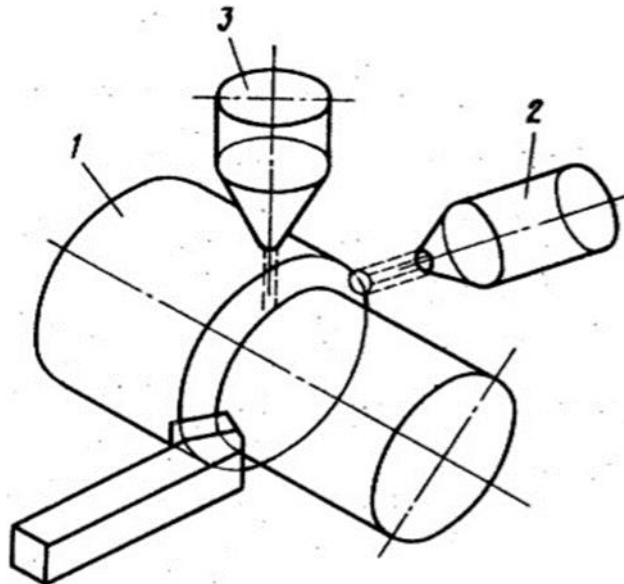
Способ механической обработки заготовок из труднообрабатываемых сталей с нагревом срезаемого слоя, где 1 – заготовка, 2 – плазмотрон, 3 – устройство для подачи охлаждающей среды [57 – 59]
